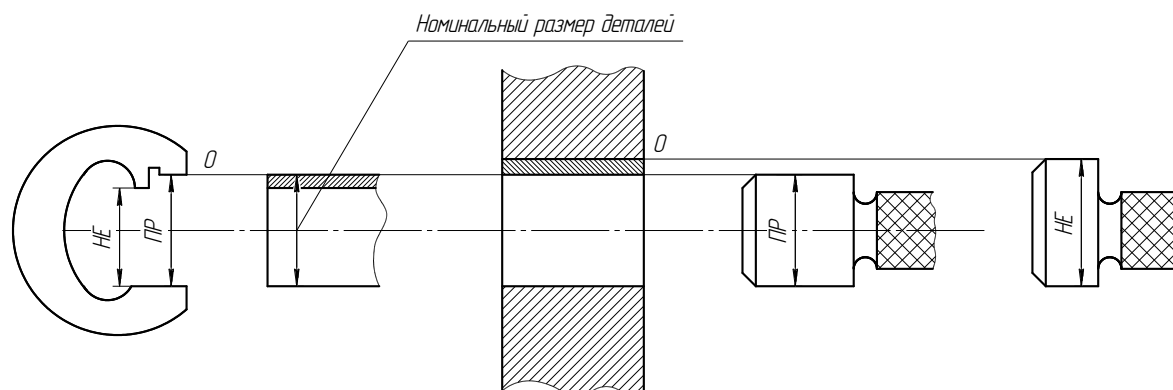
Схема контроля деталей гладкими калибрами
